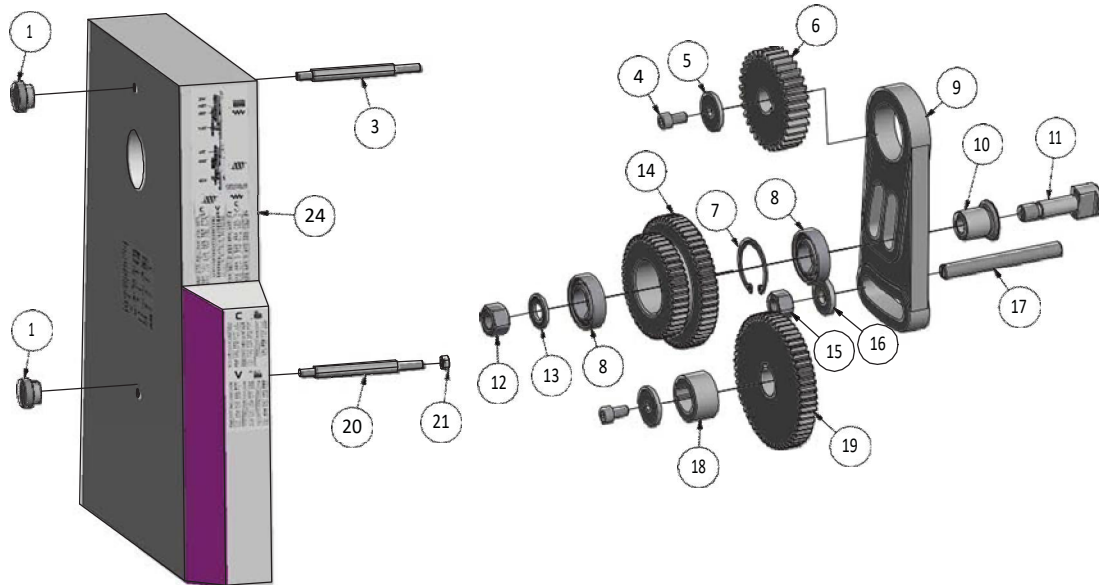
Wechselradgetriebe – Cambio engranaje rueda
